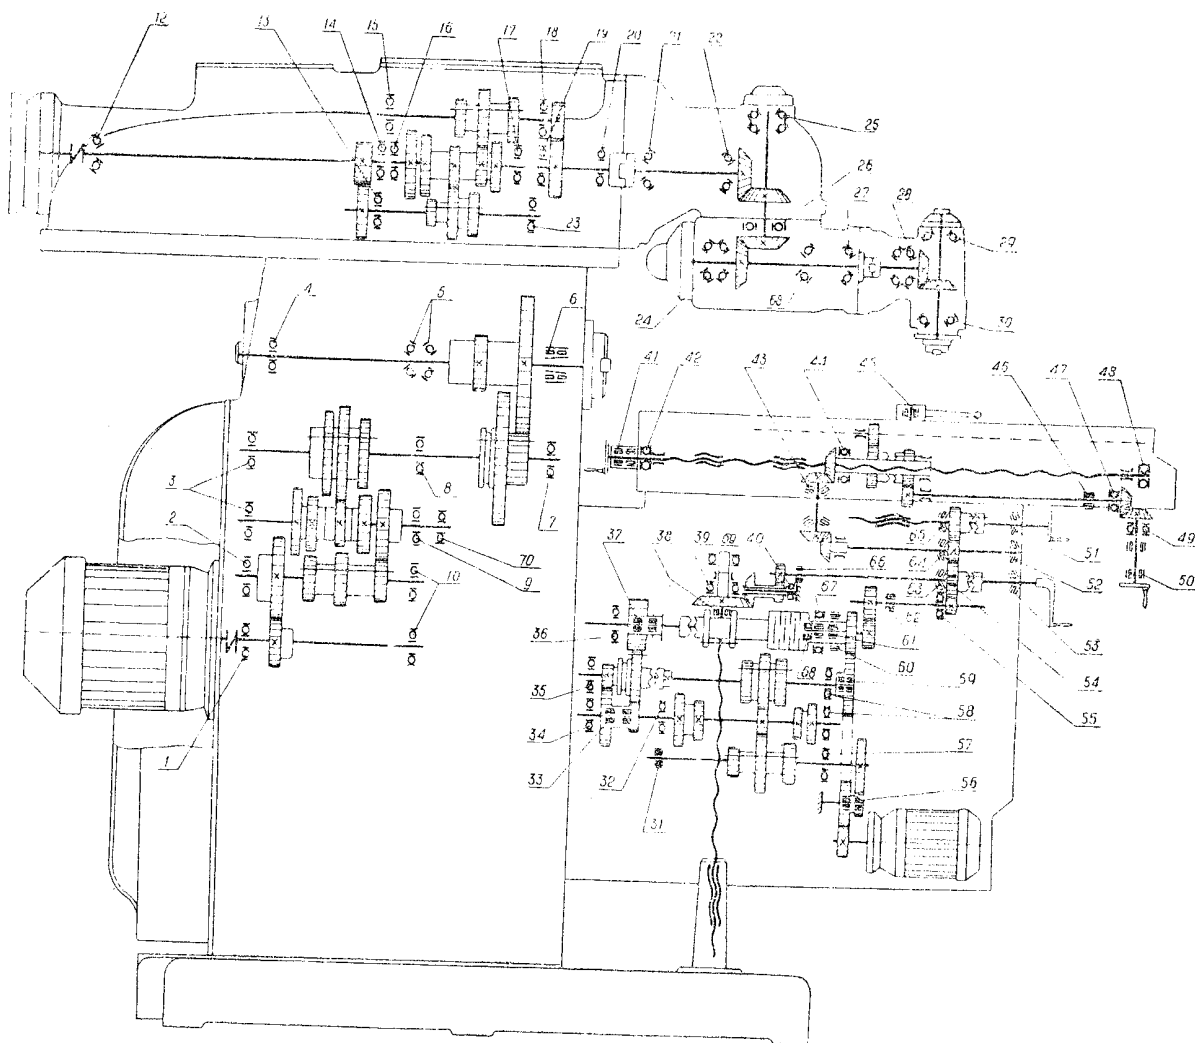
Схема расположения подшипников станка модели 6М82Ш
